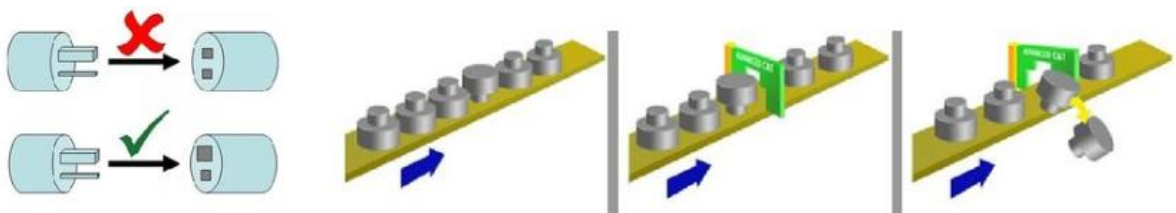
Примеры конструкций простых приспособлений для исключения ошибки установки детали
